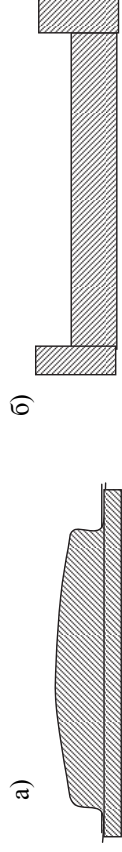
Сечения форм: а – для изготовления внутренней обшивки; б – для изготовления внешней обшивки и всей панели
